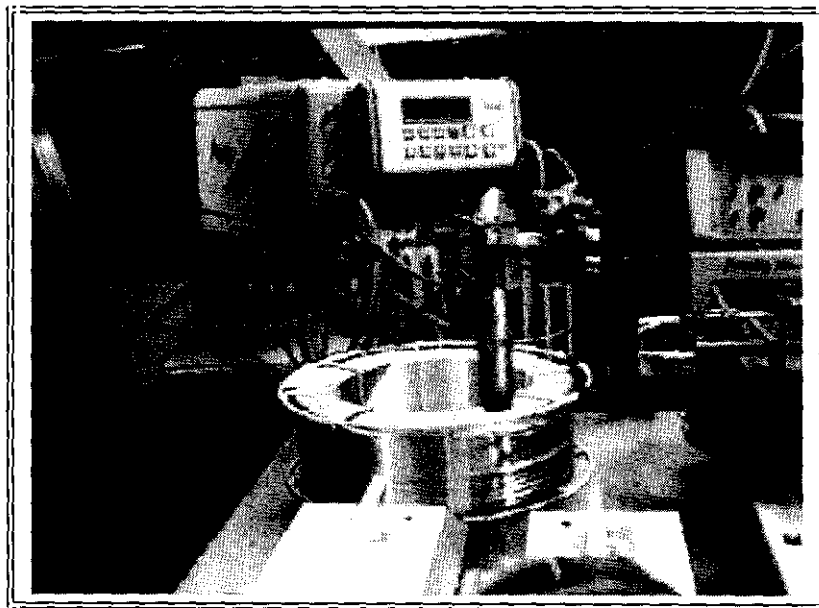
Equipo de soldadura MIG (ARISTOTIG 500).
